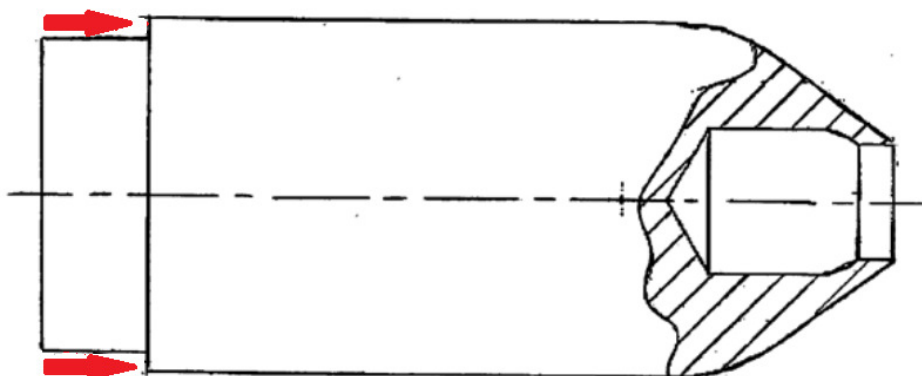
Representação do tampão terminal para solda TIG, com indicação da região que será soldada
